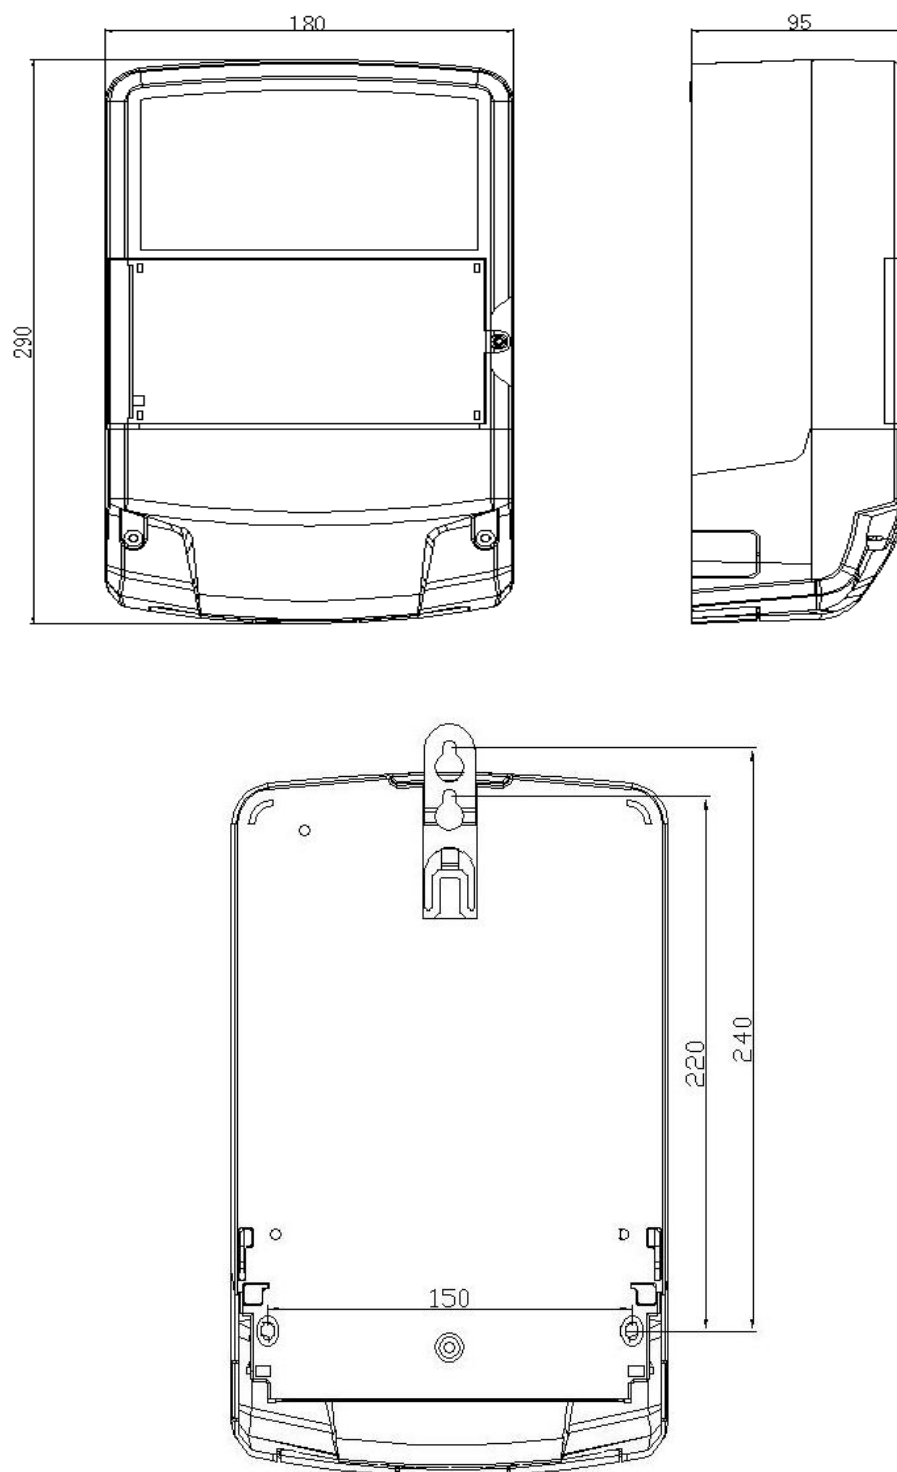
Габаритные размеры и установочные размеры концентратора ЭС-951
